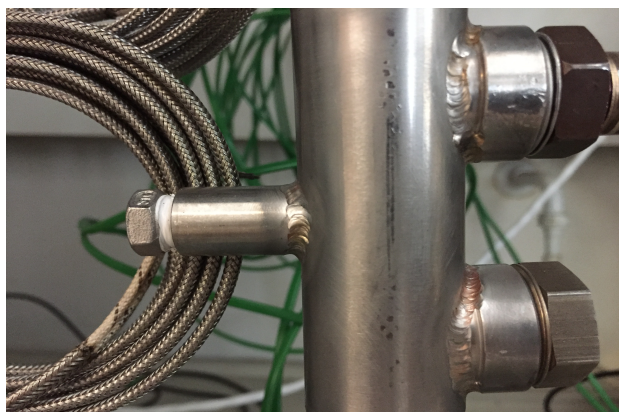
Soldadura de los casquillos de M14X1,5 y $\frac{1}{8} \text{ npt}$.
